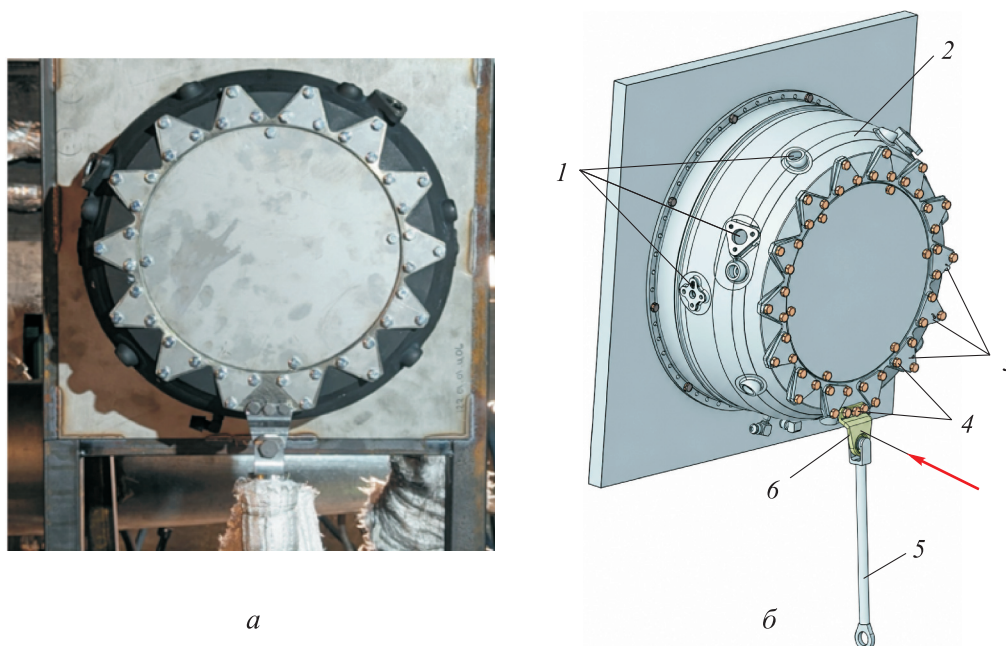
Внешний вид (а) и цифровая модель (б) корпуса КС с элементами заднего узла крепления ГТД:
